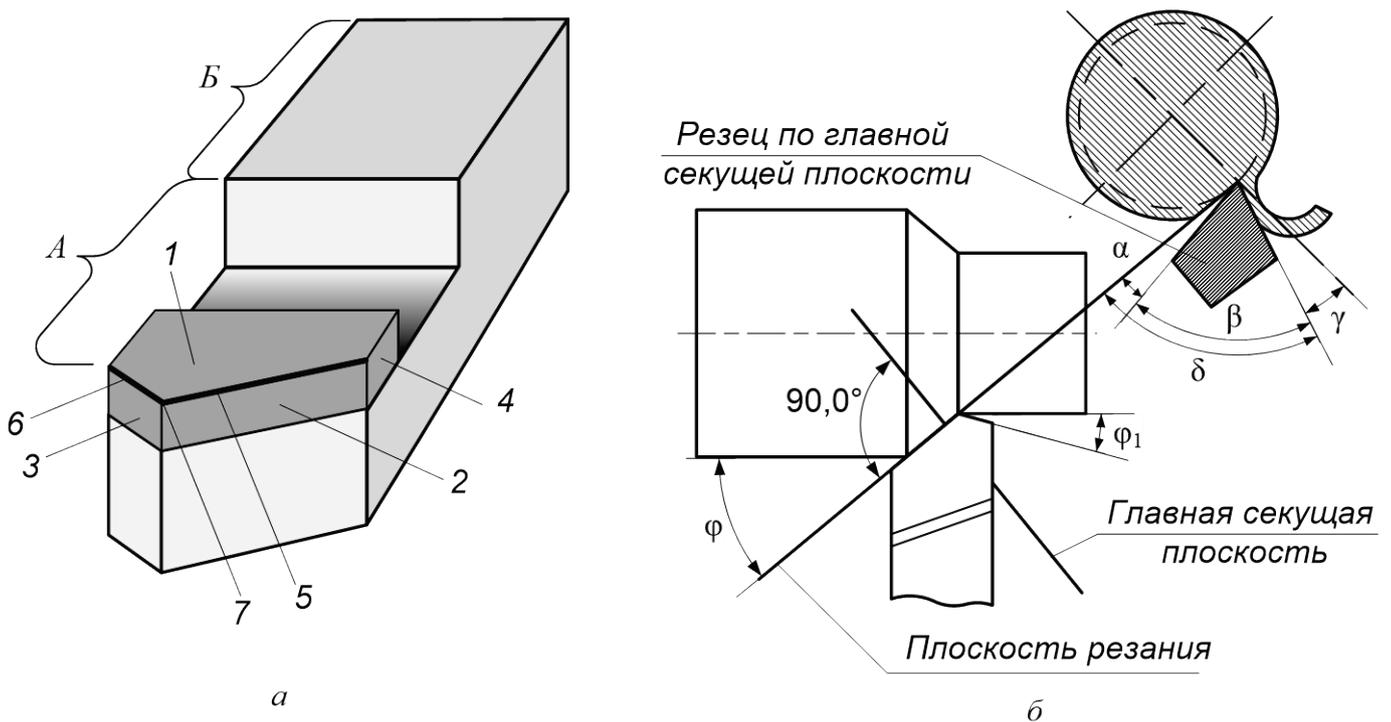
Элементы (а) и главные углы (б) токарного резца: А — режущая часть; В — стержень; 1 — передняя поверхность; 2 — главная задняя поверхность; 3 — вспомогательная задняя поверхность; 4 — пластина из твердого сплава; 5 — главная режущая кромка; 6 — вспомогательная режущая кромка; 7 — вершина режущей части; γ — главный передний угол; α — главный задний угол; β — угол заострения; δ — угол резания; φ — главный угол в плане; φ_1 — вспомогательный угол в плане
